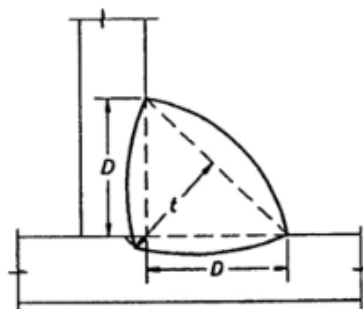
Nomenclatura para soldadura de filete en placas Gusset
